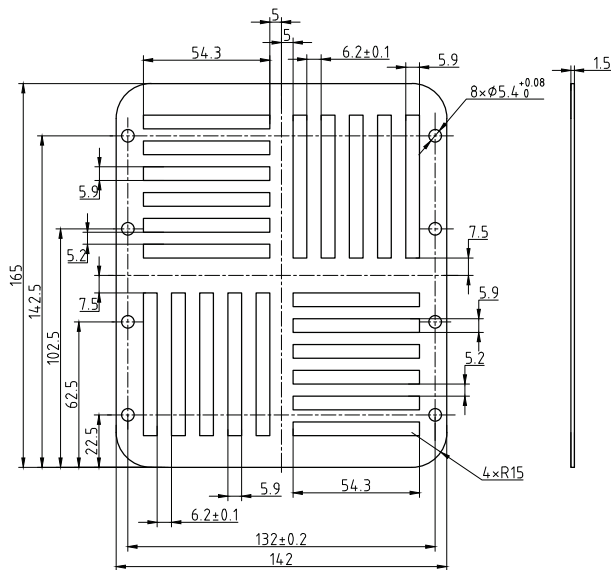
Присоединительные размеры монтажной пластины FCP-2.2S
